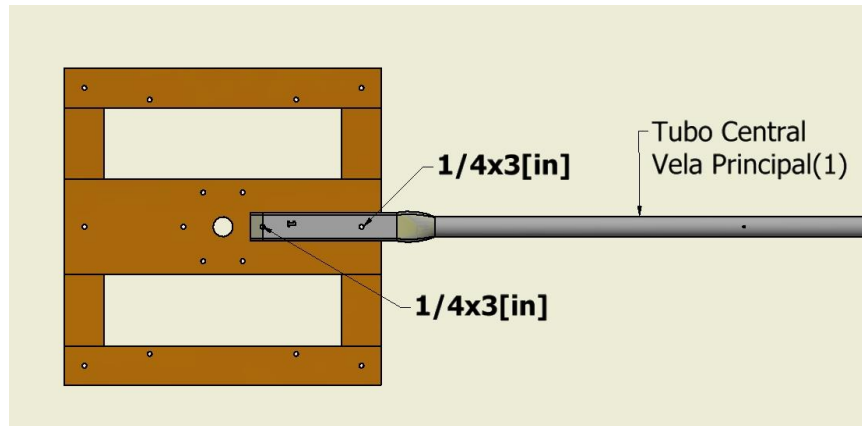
DIMENSIONES DE LA PARTE CUBO 3
